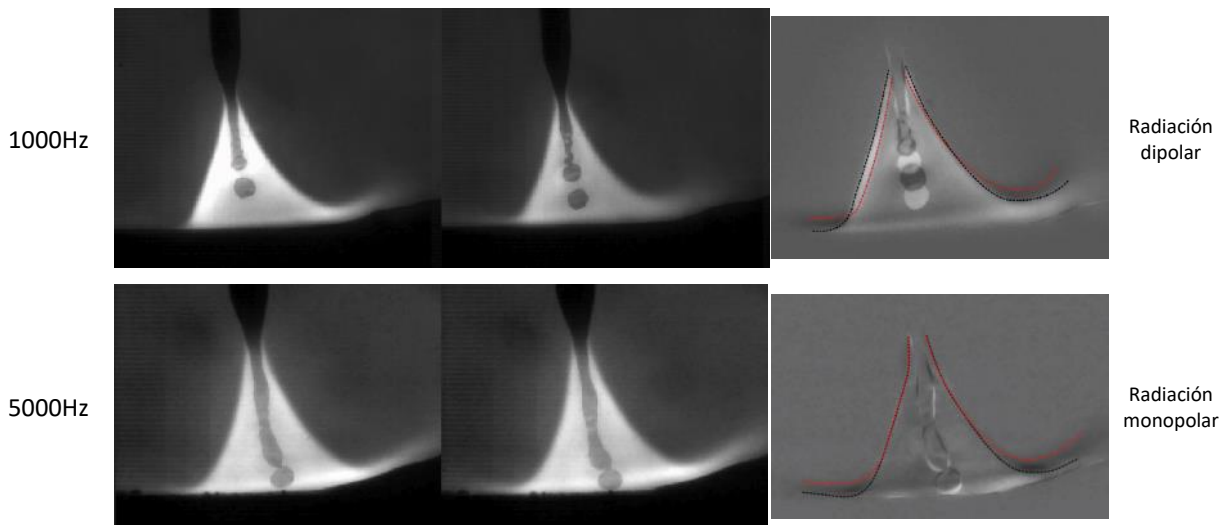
Esquema del comportamiento electromagnético del arco de soldadura
